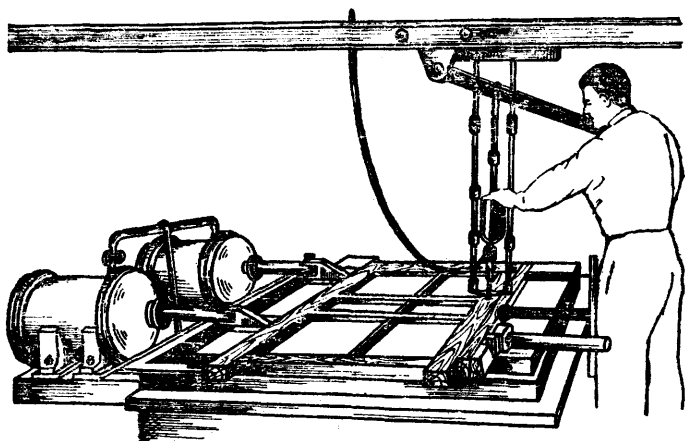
Гидравлическая вайма для запрессовки окон и дверей.
